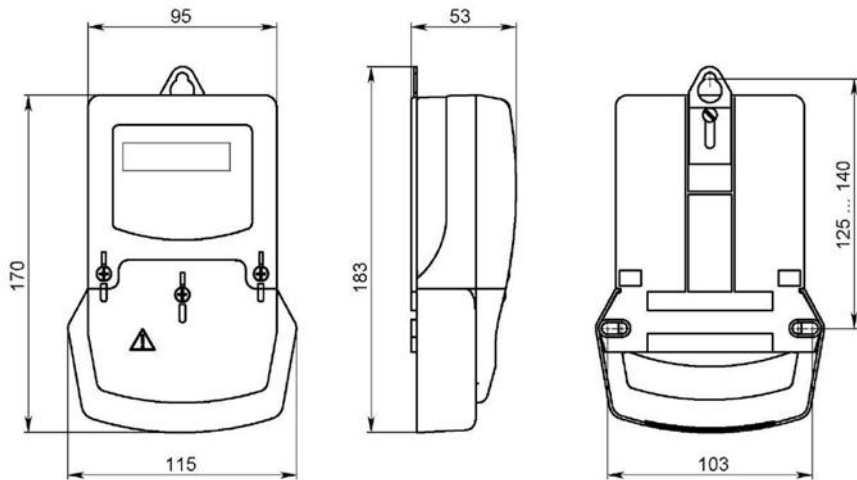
Габаритные и установочные размеры счетчика в корпусе S6
